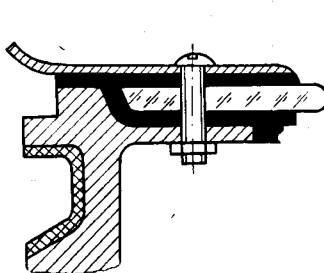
Жесткое крепление стекла к каркасу без распорной втулки.
